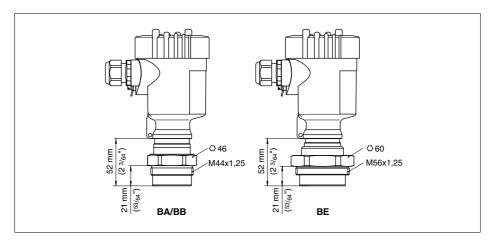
VEGABAR 64 - Gewindeanschluss für die Papierindustrie: BA/BB = M44 x 1,25, BE = M56 x 1,25
